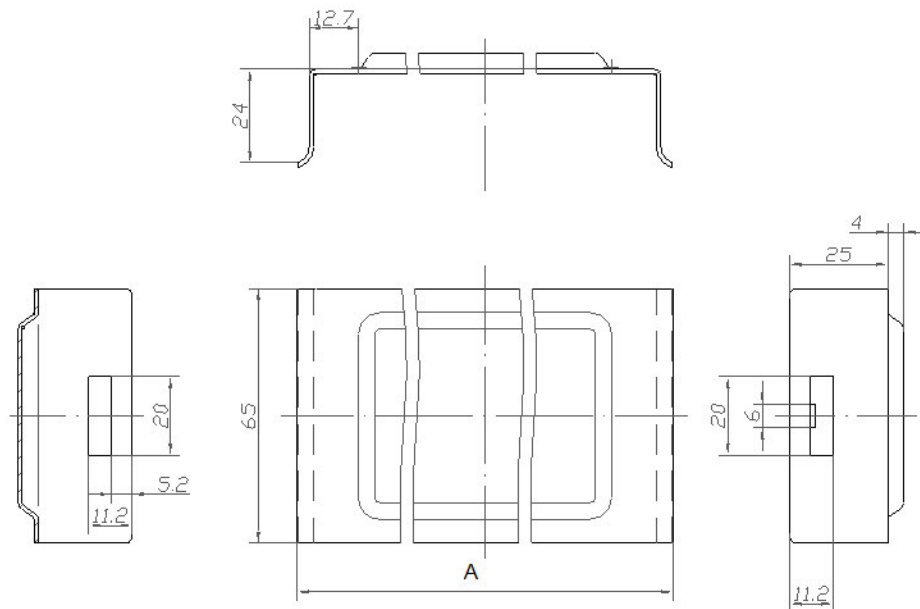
Пластина защитная боковая IP44, типов: 30571, 30580, 30574
